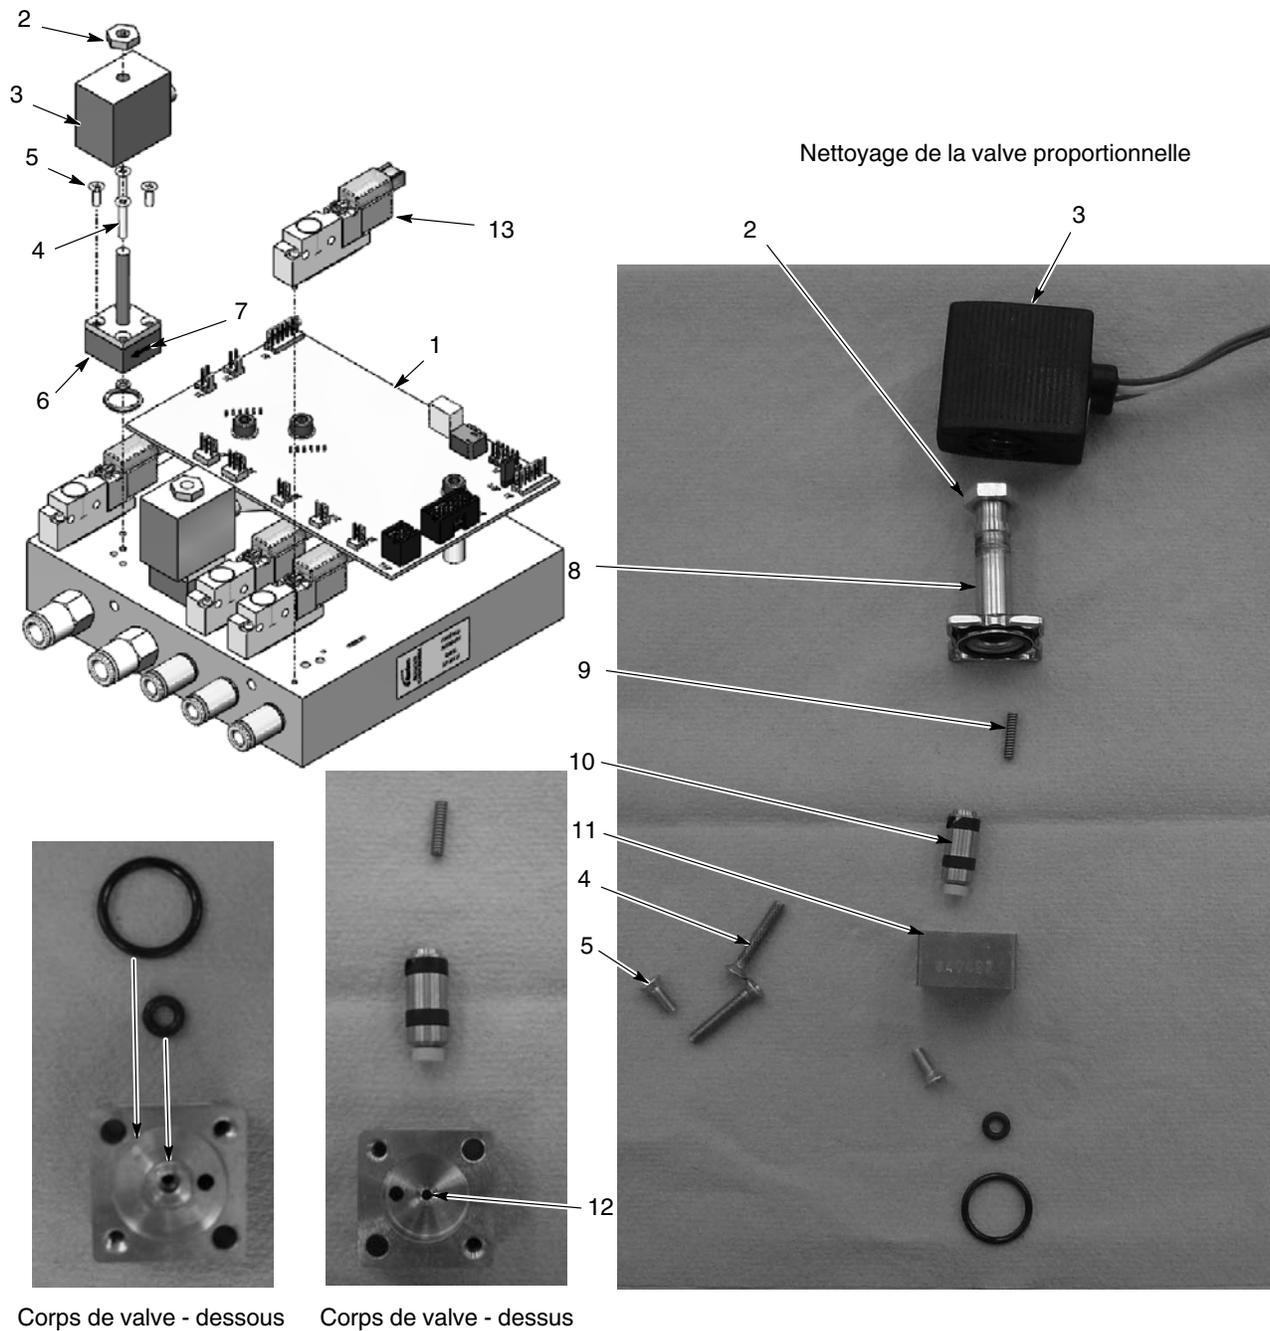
Réparation du module iFlow - Remplacement de l'électrovanne et nettoyage ou remplacement de la valve proportionnelle
